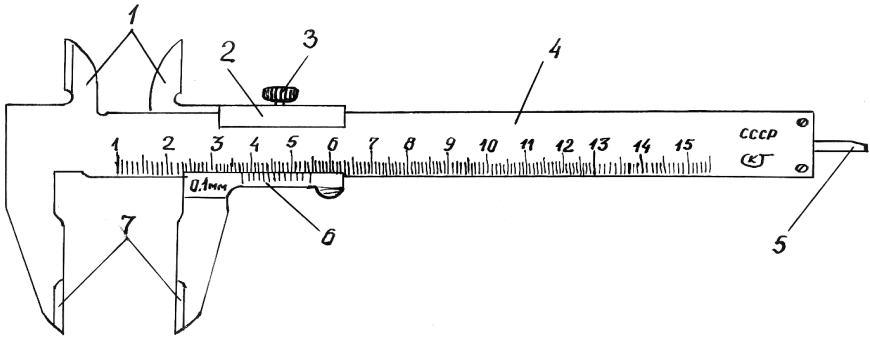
Штангенциркуль ШЦ-I: 1 – губки для внутрішніх вимірювань; 2 – рамка; 3 – затискач рамки; 4 – штанга; 5 – лінійка глибиномірна; 6 – ноніус; 7 – губки для зовнішніх вимірювань
